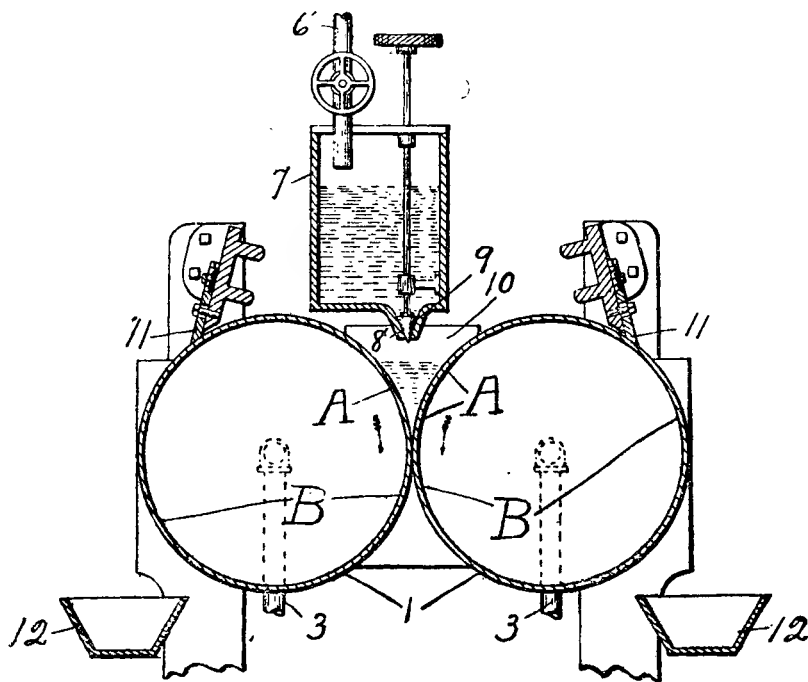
Машина для изготовления сухого молока конструкции John A. Just.
